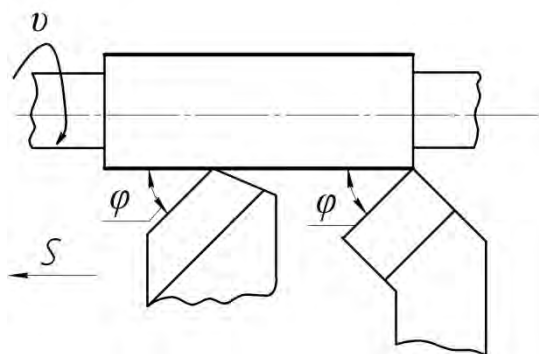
Схема обработки прямыми и отогнутыми проходными резцами
